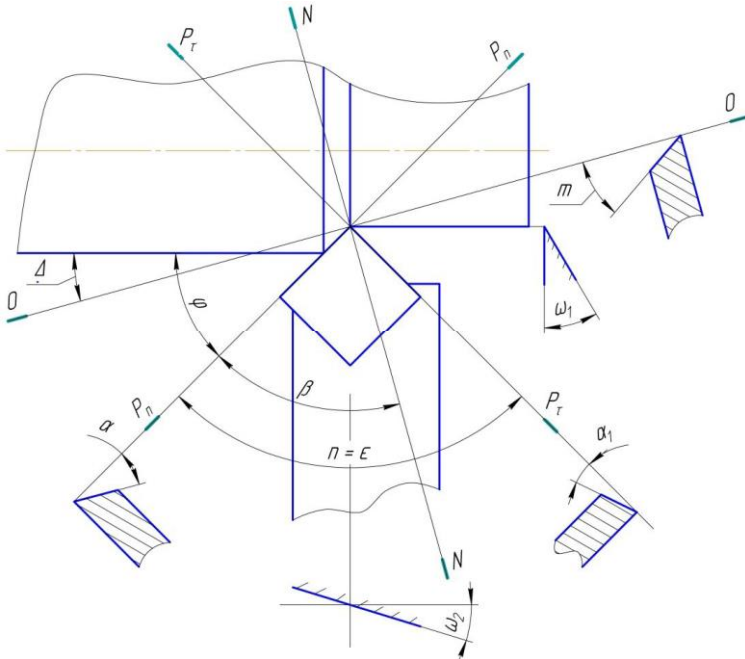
Схема розташування опорної поверхні пластинки на державці різця
